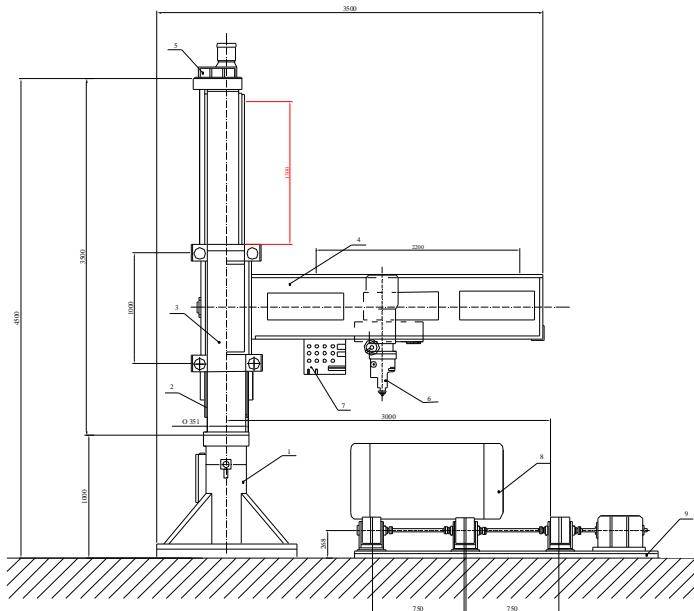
Эскиз установки для сварки кольцевых швов корпуса.
